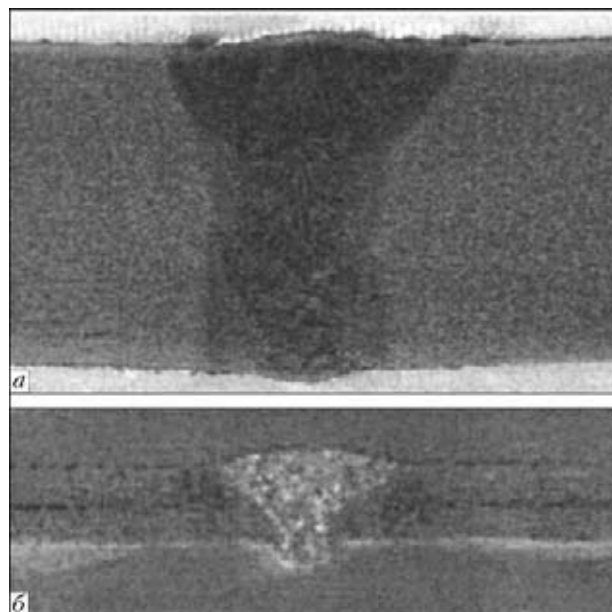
Макроструктура стыковых соединений, выполненных лазерно-дуговой сваркой: а — сталь Х70 толщиной 18,7 мм, четыре прохода (мощность излучения 2,7 кВт; скорость сварки 25 м/ч; скорость подачи проволоки 400 м/ч,  $\varnothing$  1,2 мм; ток сварки 200 А; напряжение 25 В; защита —  $\text{CO}_2$ ),  $\times 2,5$ ; б — сплав АМг6 толщиной 1,9 мм (мощность излучения 2,5 кВт; скорость сварки 300 м/ч; скорость подачи проволоки 760 м/ч; ток сварки 200 А; защита — Ar),  $\times 5$
